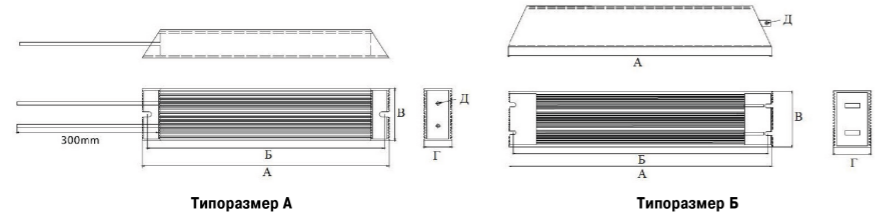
Габаритно-установочный чертеж резисторов серии РБ3
